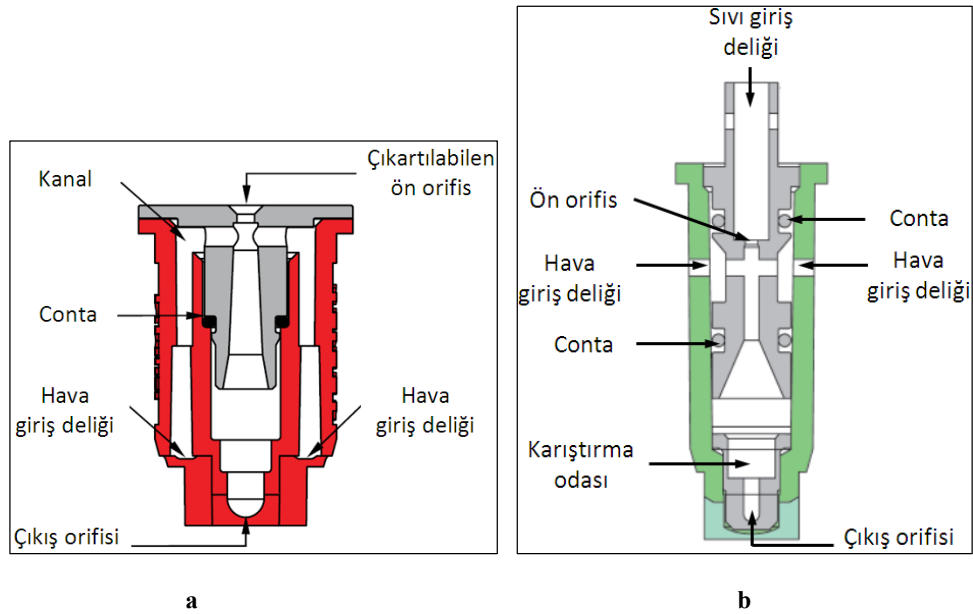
Denemelerde kullanılan püskürtme memeleri.
